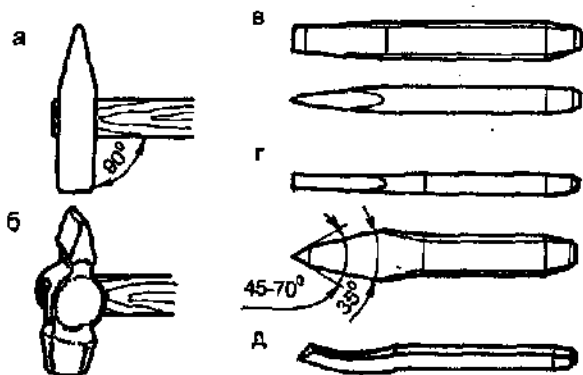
Инструменты для рубки: а — слесарный молоток с квадратным бойком; б — слесарный молоток с круглым бойком; в — слесарное зубило; г — крестовидный инструмент; д — канавочник
